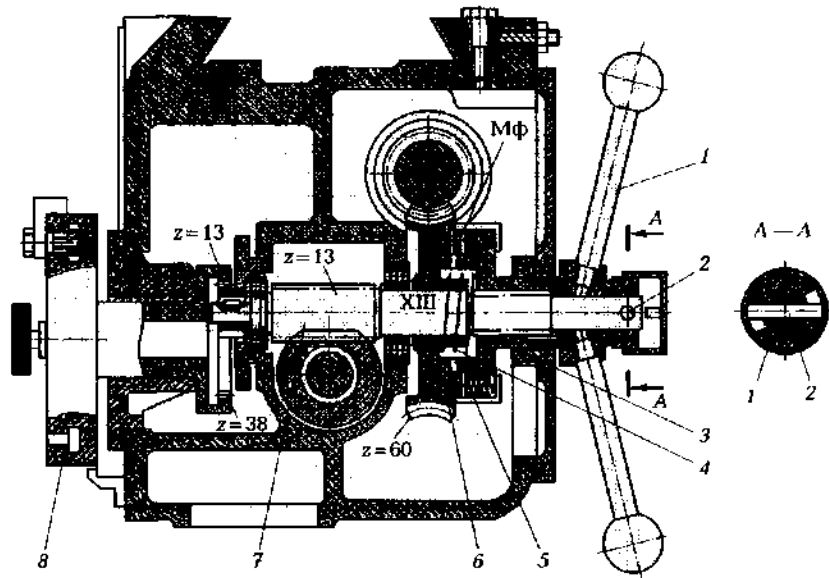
Механизм перемещения шпинделя в вертикально-сверлильных станках:
